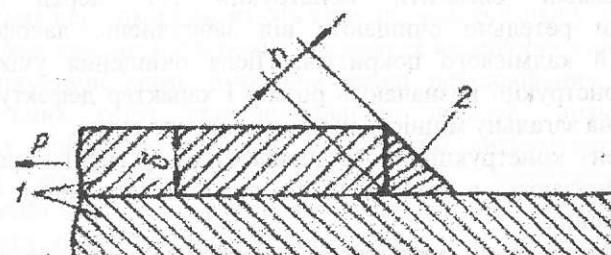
Зварний шов внакладку: 1 – деталі, що зварюються; 2 – зварний шов; h – висота зварного шва; δ – товщина деталей, що зварюються
